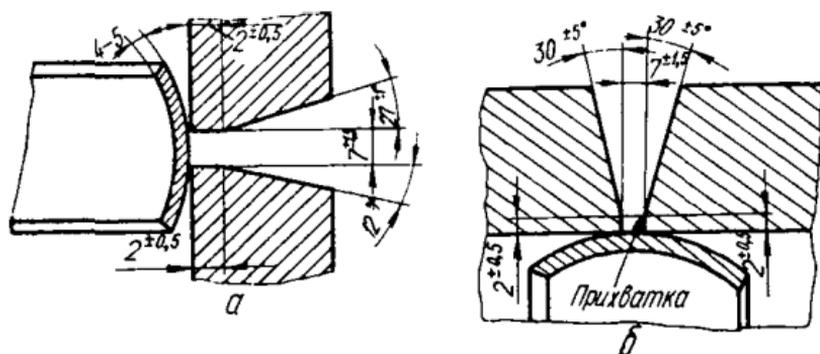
Подготовка под сварку кольцевых стыков:
